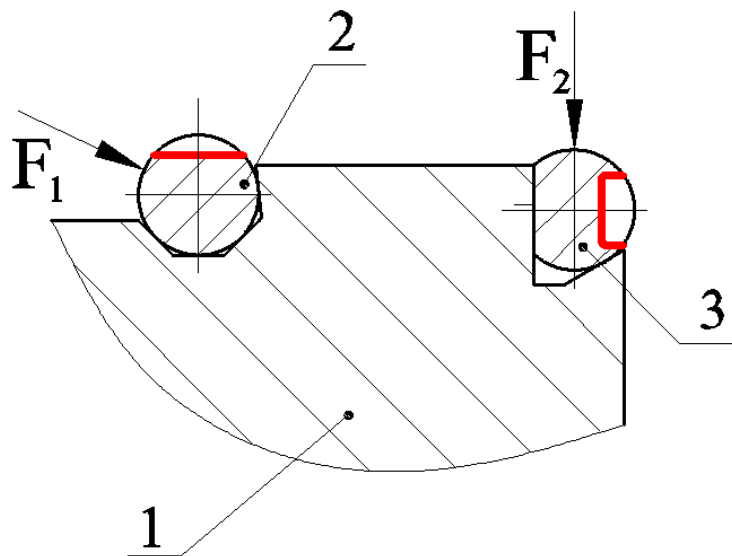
Схема приспособления для фрезерной обработки детали типа «Стойка»
